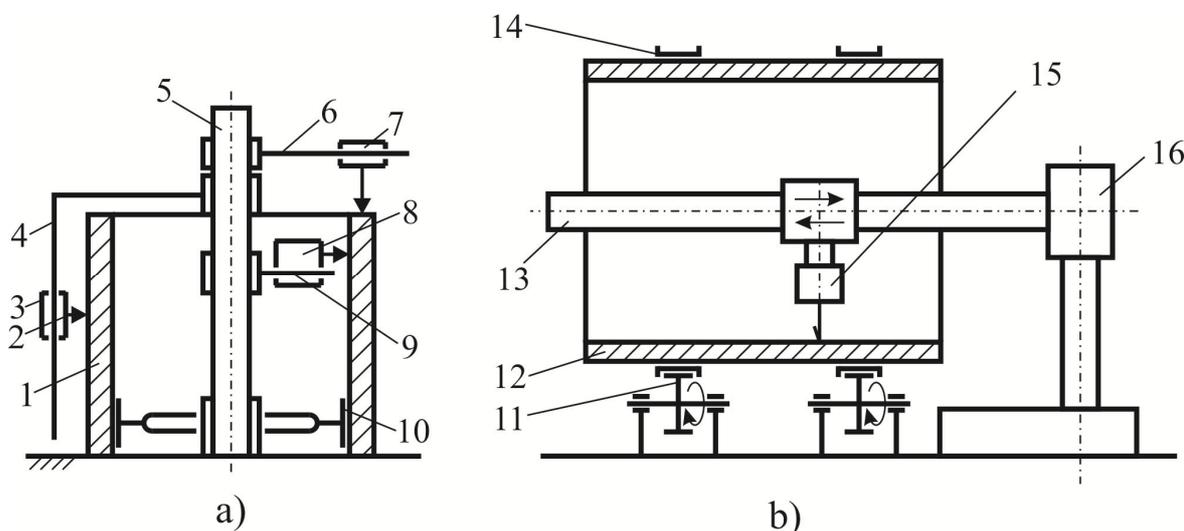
Схема вариантов применения мобильных металлообрабатывающих блоков при механической обработке обечайки и блоков сварочного оборудования:
